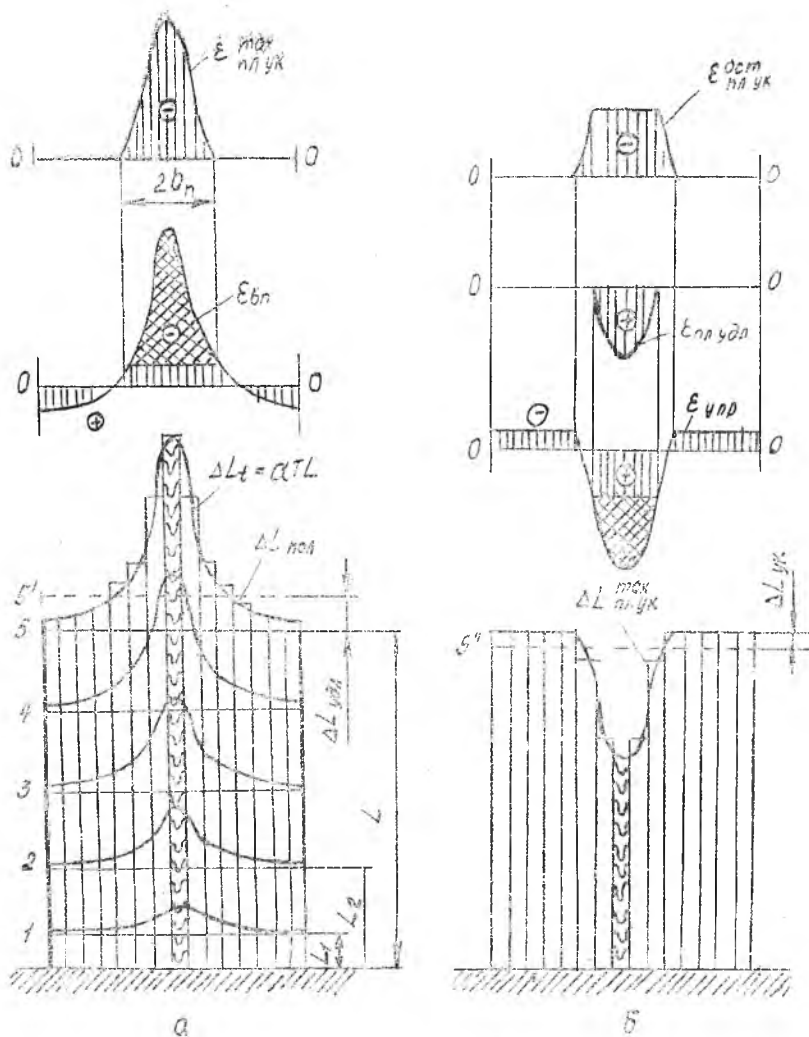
Механизм образования деформаций (а) и напряжений (б) при сварке
